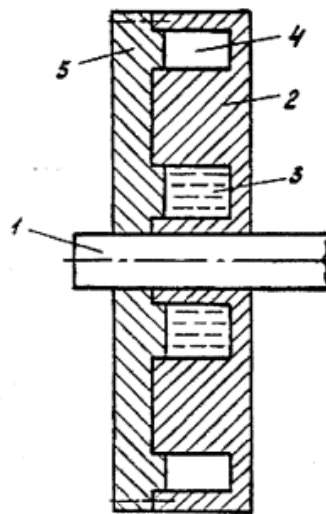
Механізм для вимірювання кутової швидкості вала в торцевому перерізі
